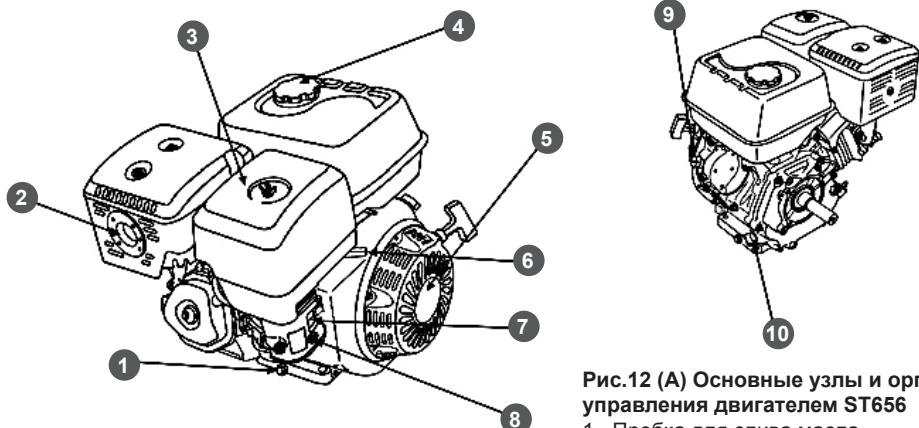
(А) Основные узлы и органы управления двигателем ST656
